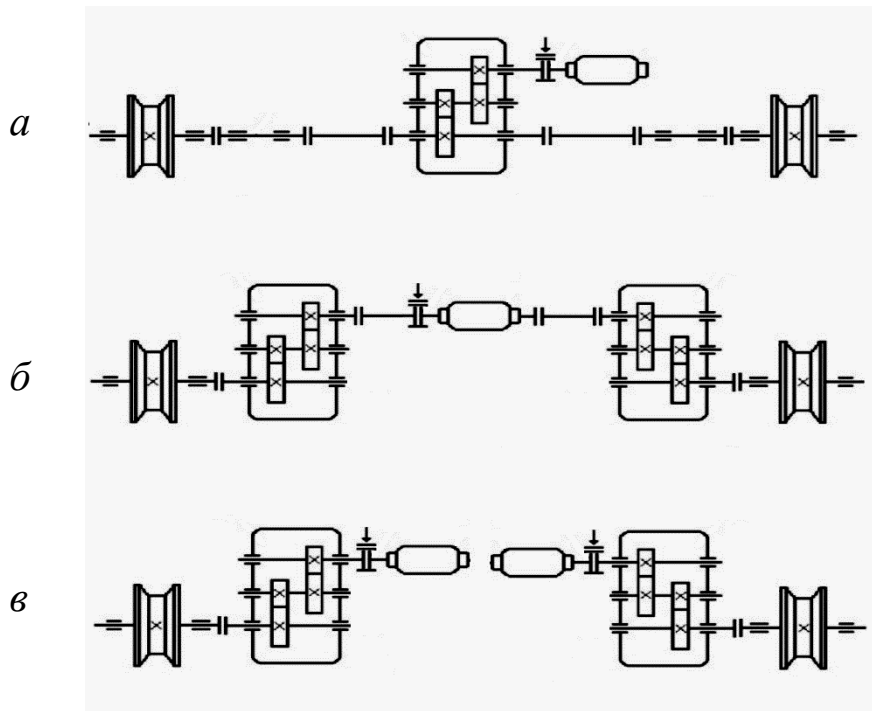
Схеми механізмів пересування з приводними колесами
